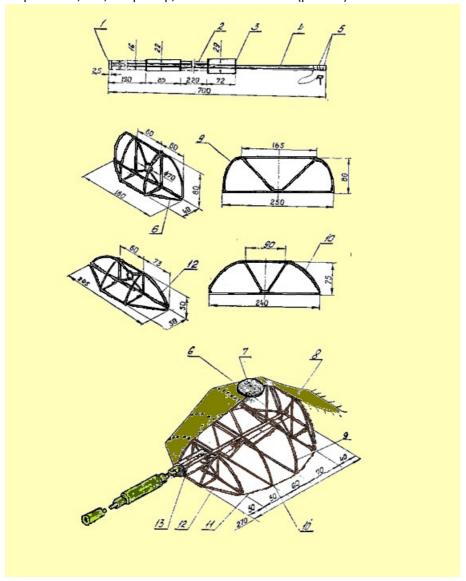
Макет башни танка, изготовленный из круглой стали и ткани
